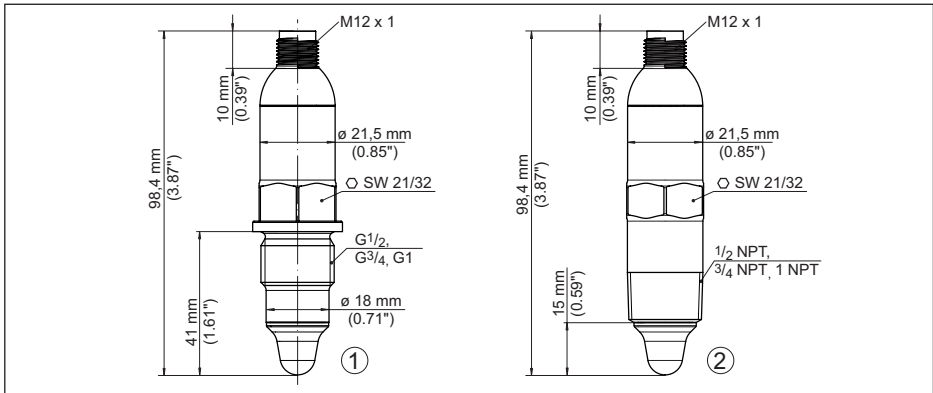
VEGAPOINT 11, Standardausführung - Gewinde
